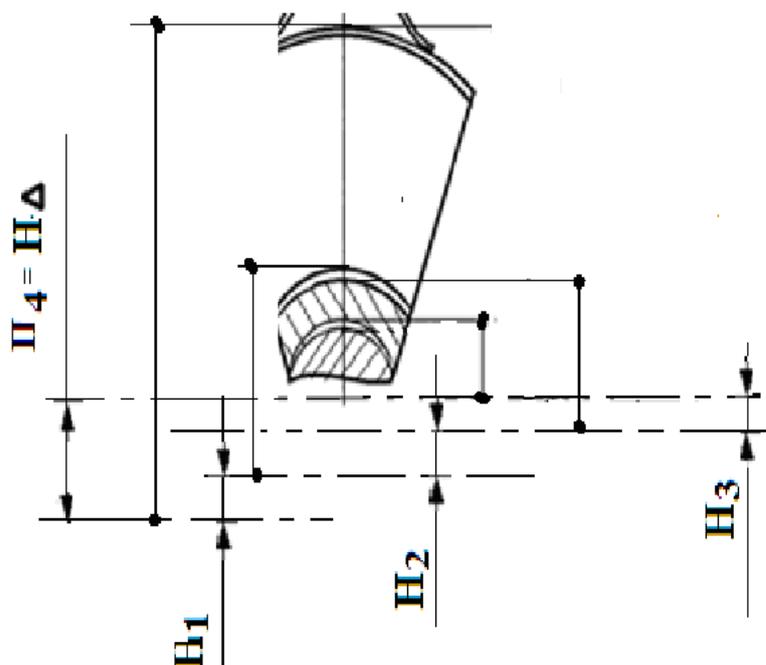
Размерная цепь формирования радиуса расположения вершин рабочего профиля бичей
